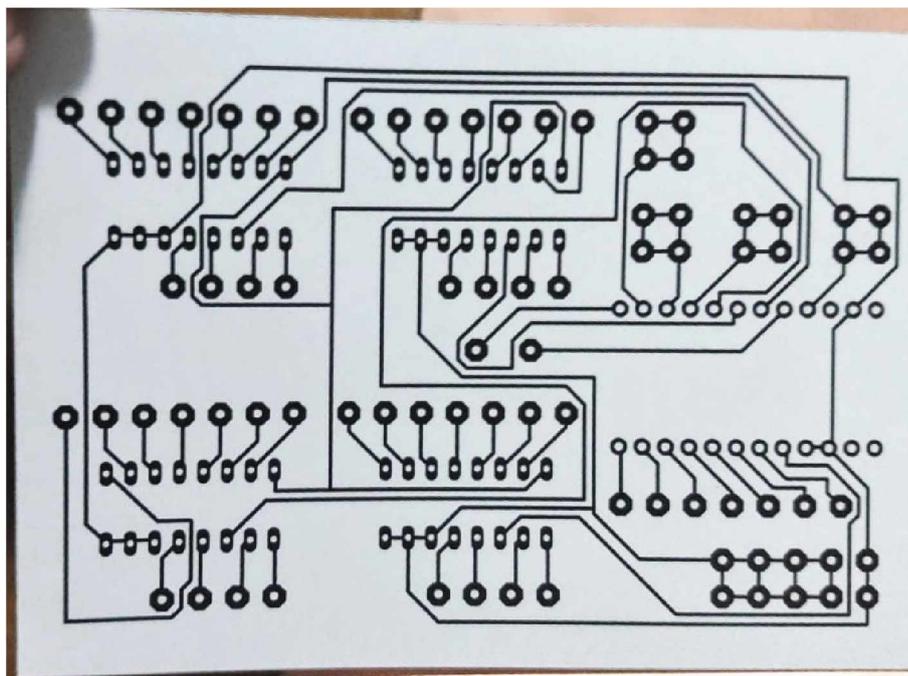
Desenho da placa impresso em papel transfer. Fonte: autoria própria
